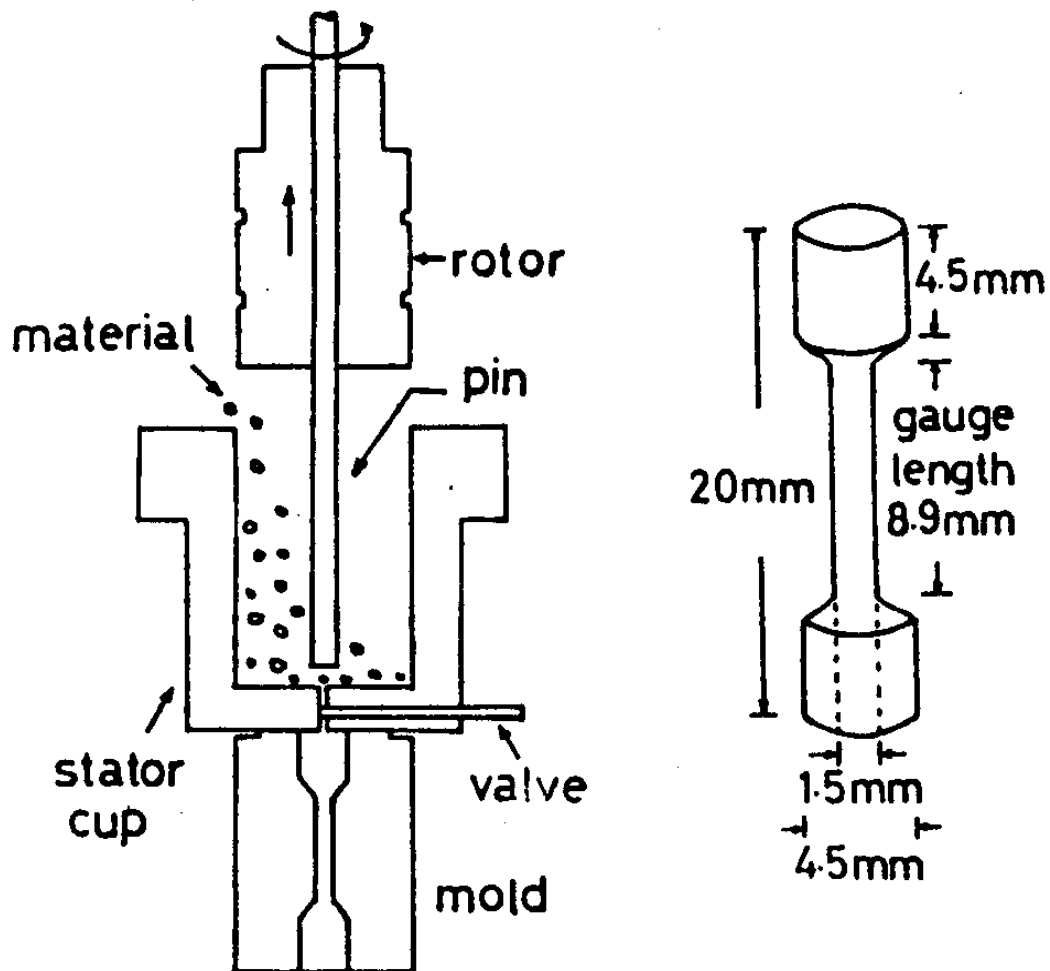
Mini-Max Injection molder를 이용한 혼합 및 사출과정 및 dumb-bell형 시편의 치수.
